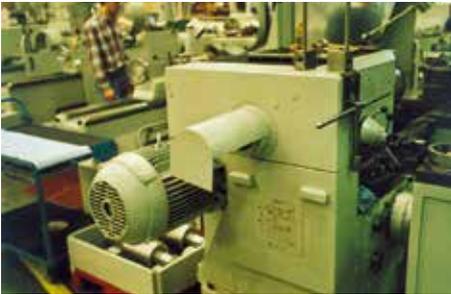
Spänefangvorrichtung an einer Drehmaschinenhohlwelle
